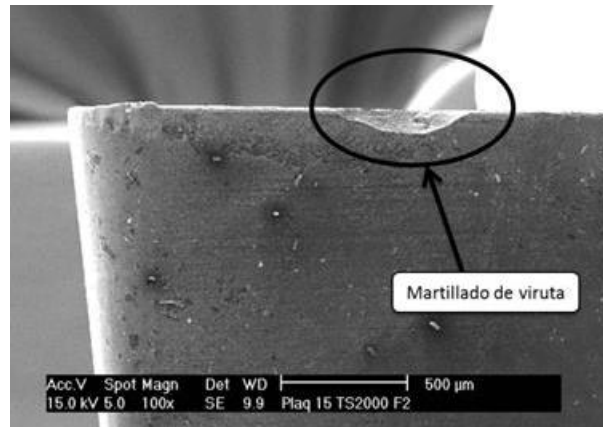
Herramienta TS2000 F2 0° ensayada a 70m/min en condiciones de seco.
